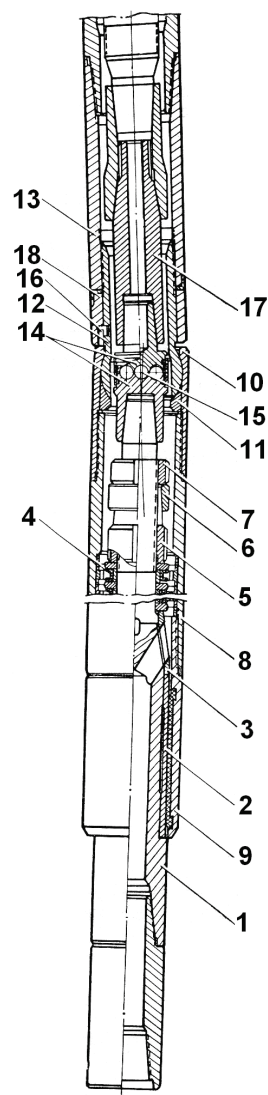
Турбинный шарнирный отклонитель ОТС-7½"
